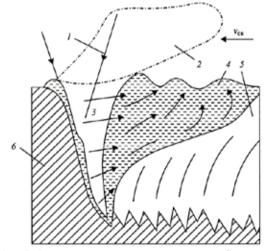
Схема продольного сечения сварочной ванны: 1 – лазерное излучение, 2 – плазменный факел, 3 – парогазовый канал, 4 – хвостовая часть сварочной ванны, 5 – закристаллизовавшийся металл, 6 – свариваемый материал
